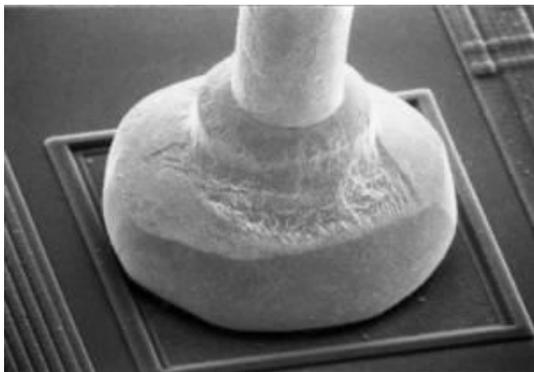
Фото сварного соединения шарик (СЭМ)
